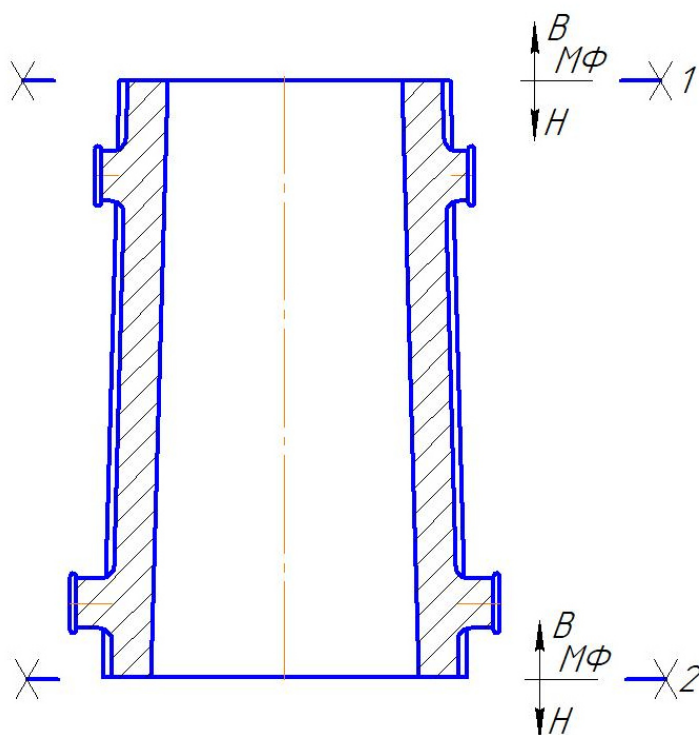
Разъем формы для отливки «Изложница»
